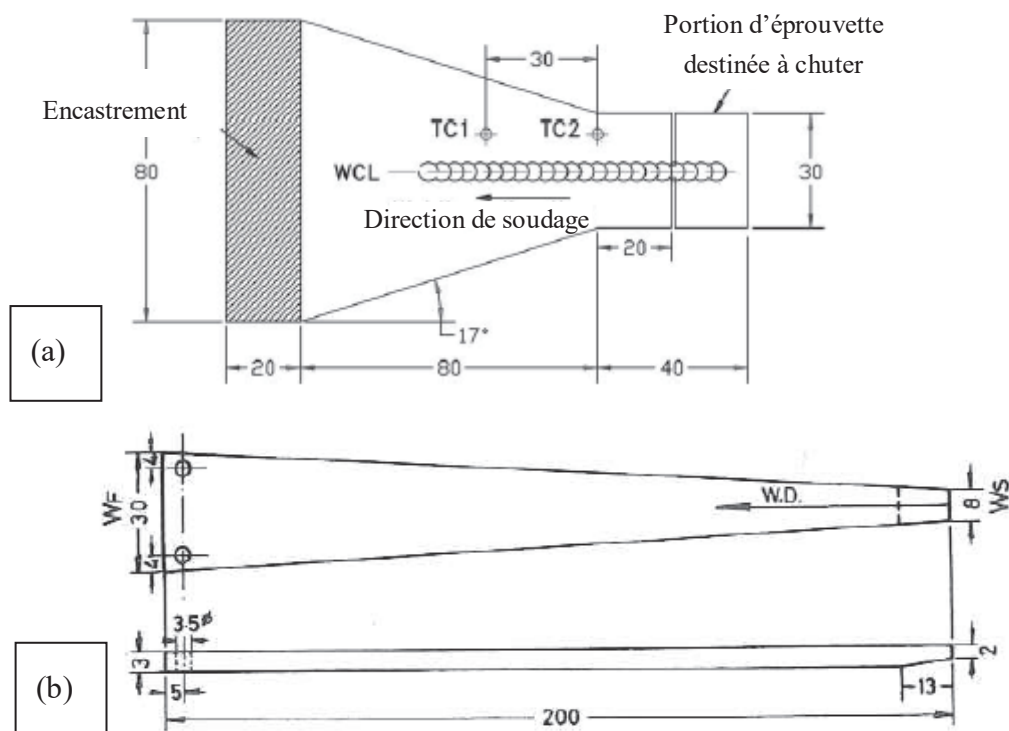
Géométries d'éprouvette d'essais trapézoïdaux : (a) adapté par Safari pour l'étude de la fissuration à chaud de l'acier inoxydable 310s en soudage TIG [97] ; (b) adapté par Matsuda en soudage par faisceau d'électrons [78]
